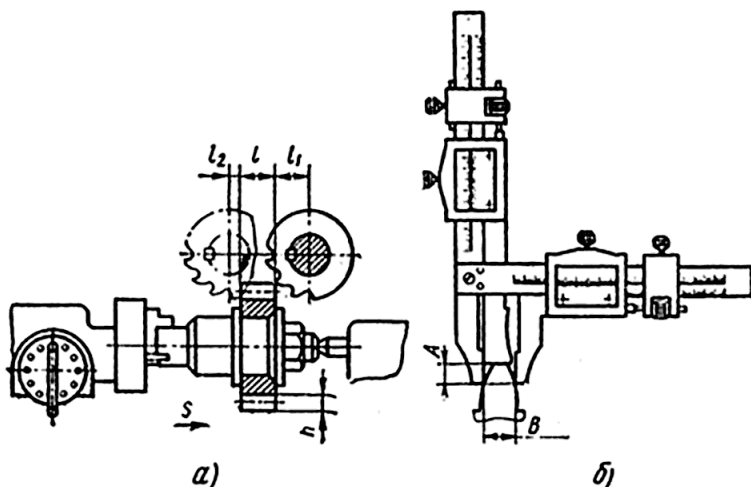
Схемы фрезерования зубьев шестерен (а) и контроля толщины зубьев (б):
